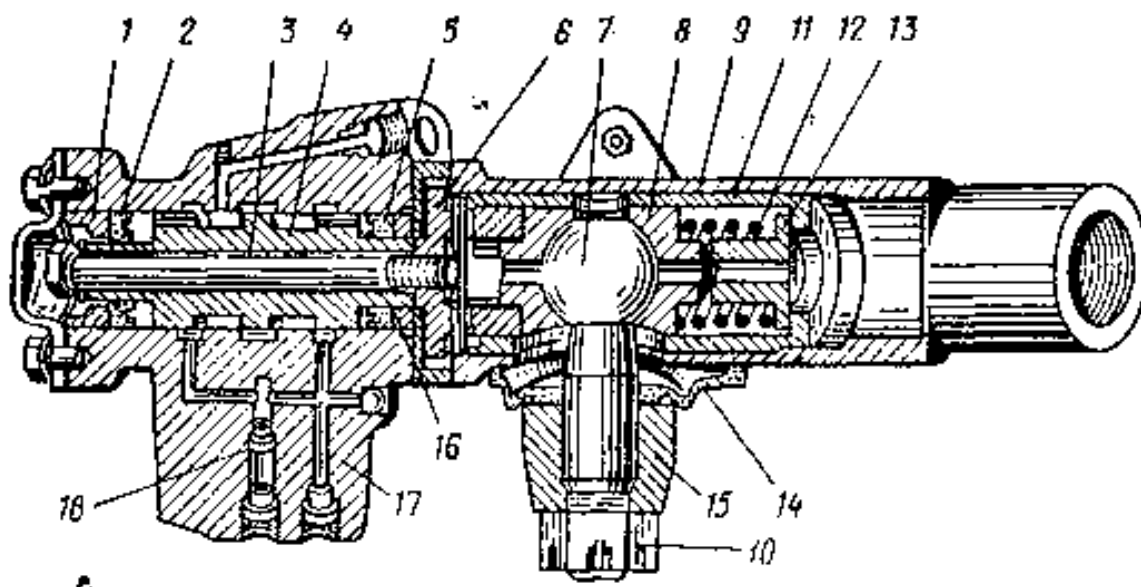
Рулевой механизм (редуктор) УАЗ-469
